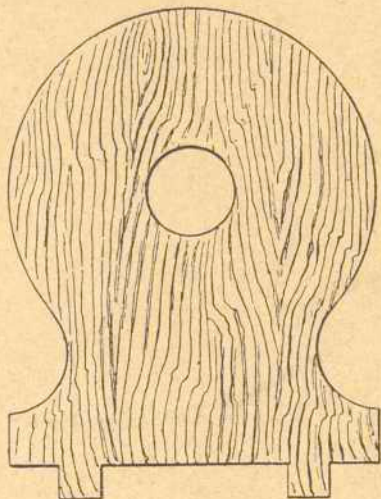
Pieza extrema del marco de una bobina de Ruhmkorff.
